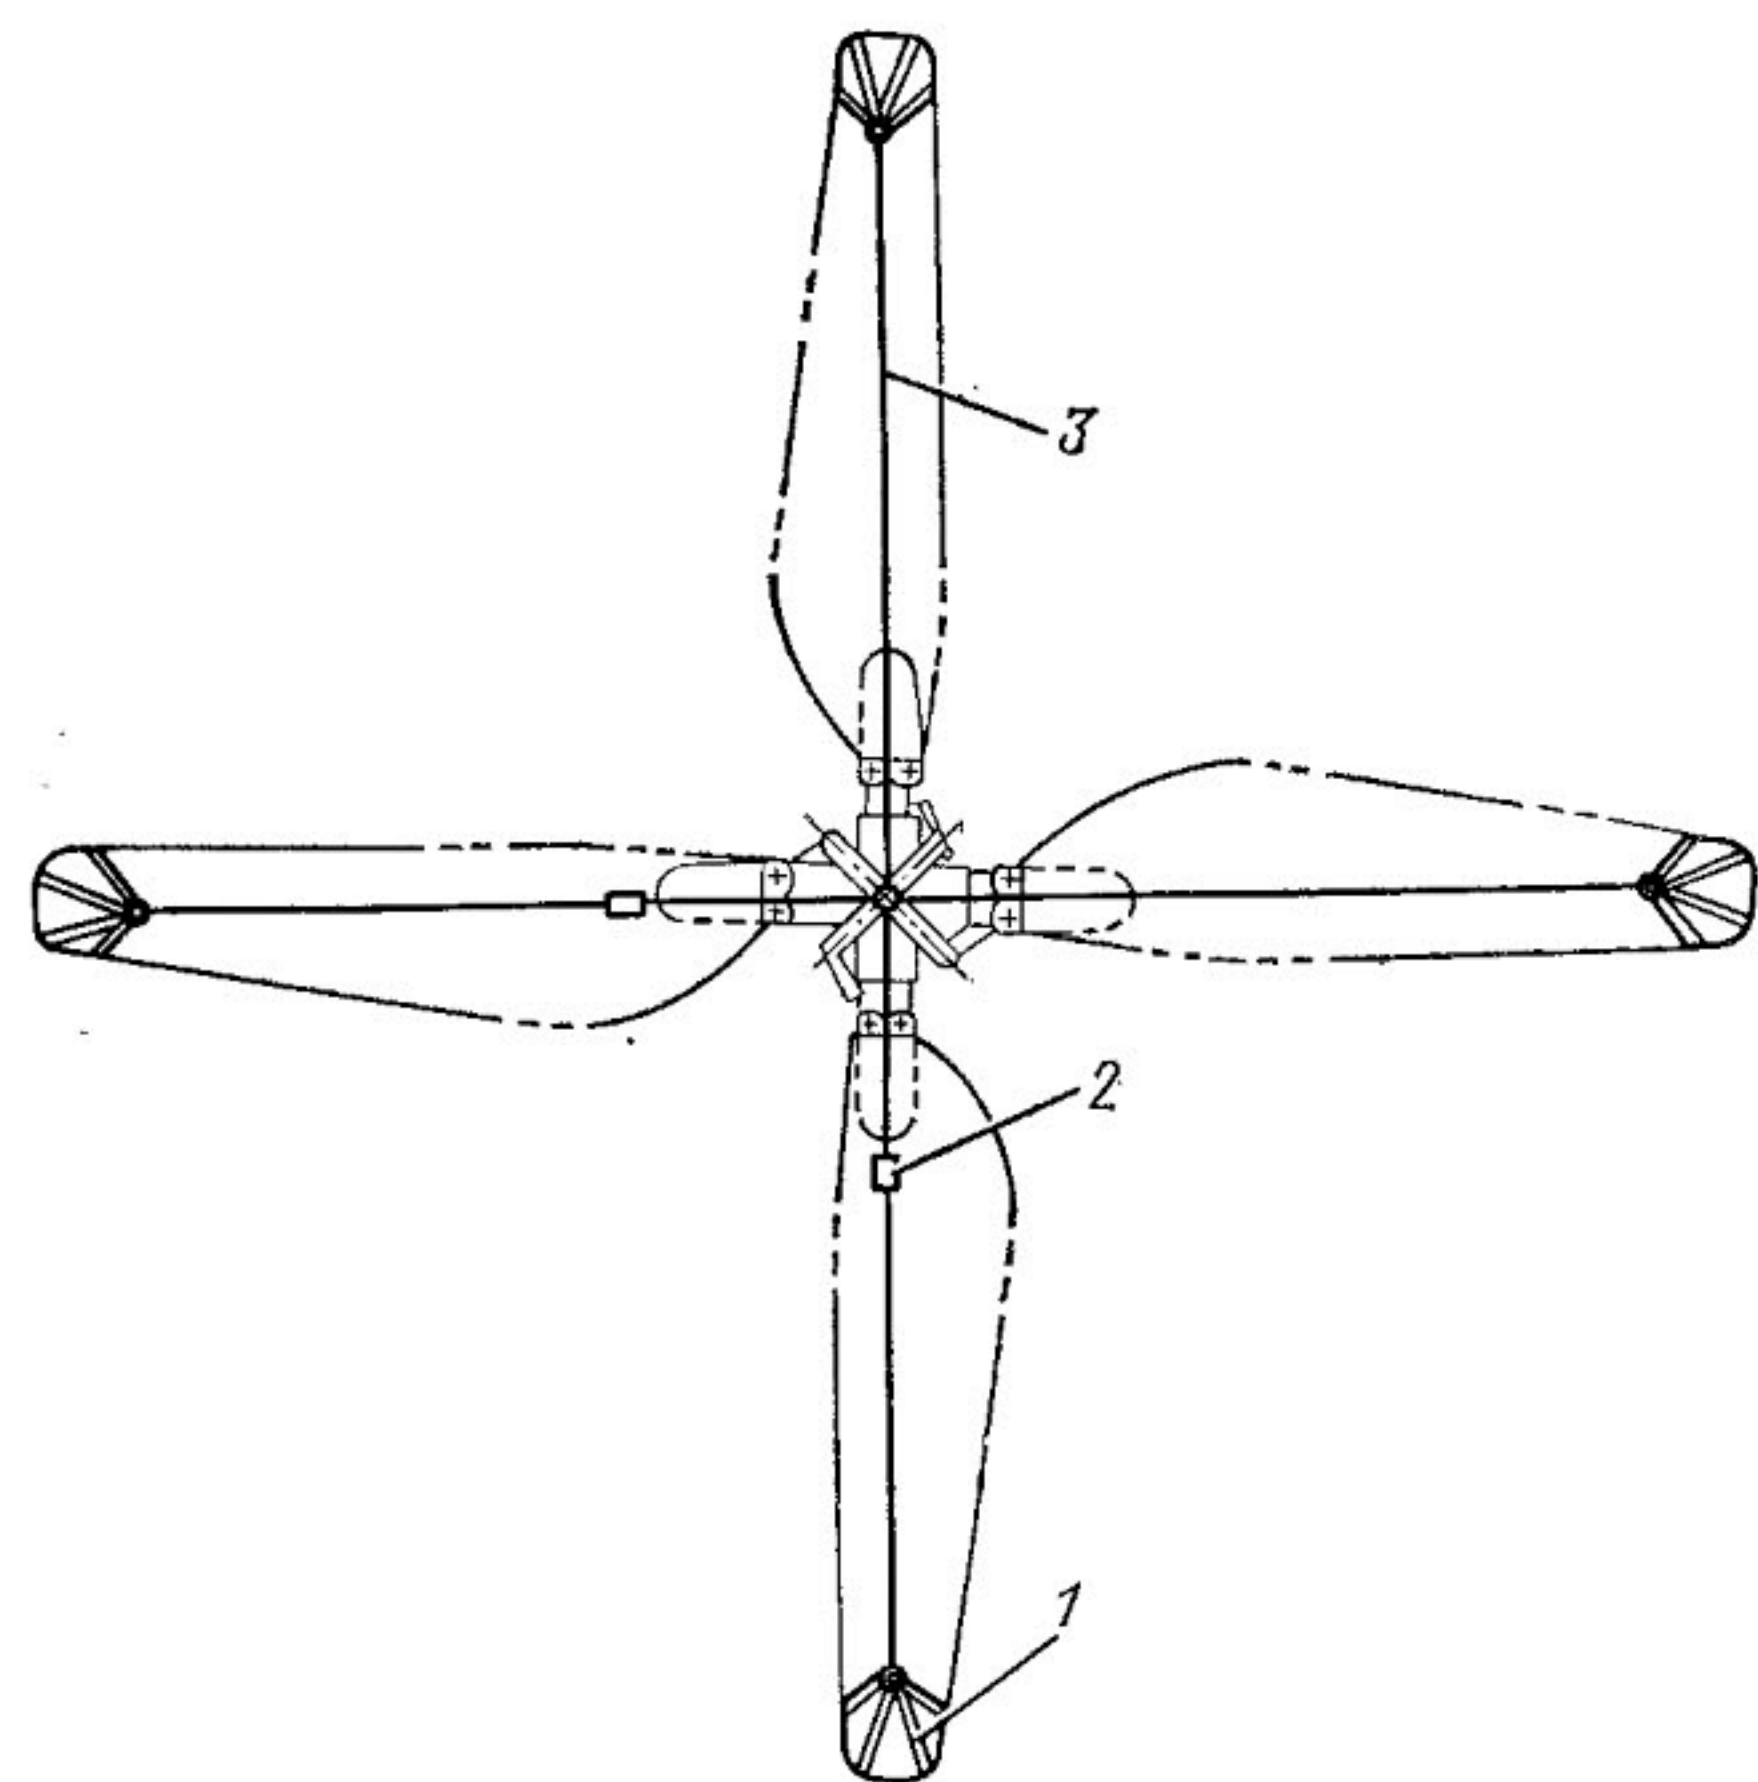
Приспособление для швартовки лопастей хвостового винта:
